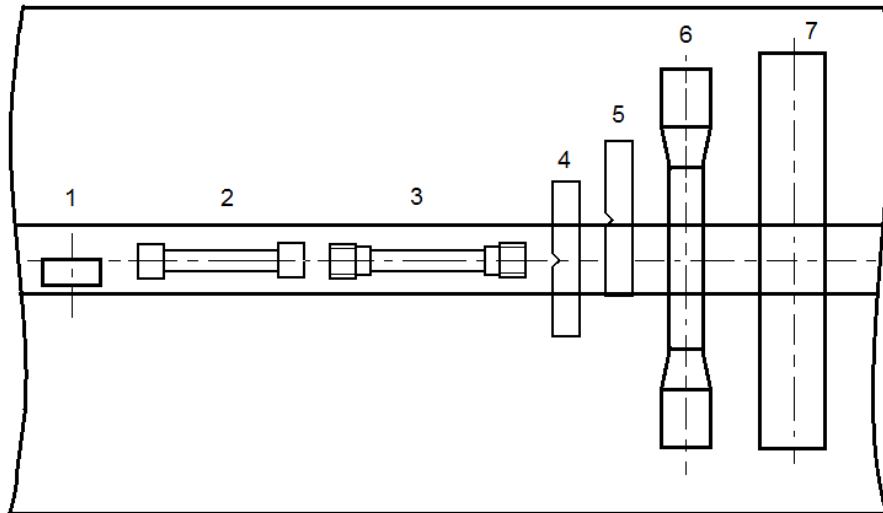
Схема вырезки образцов из металла шва и сварного соединения для:
